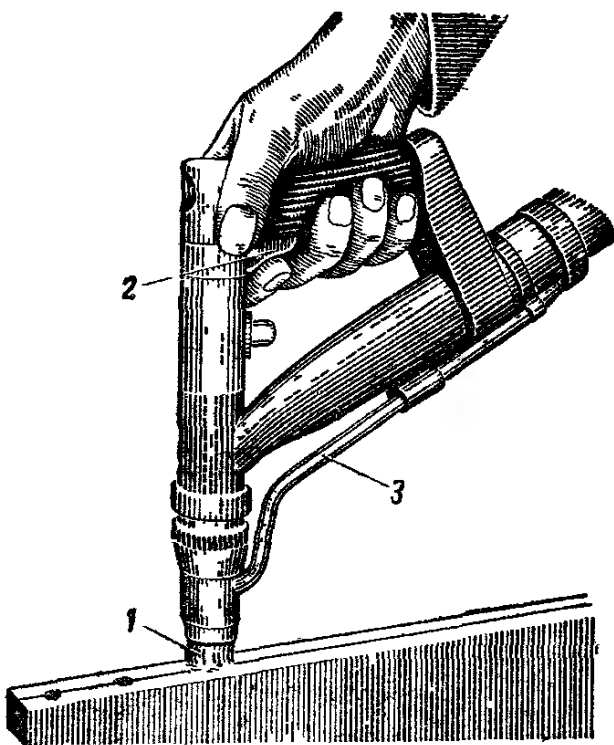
Горелка-пистолет для точечной аргоно-дуговой сварки
